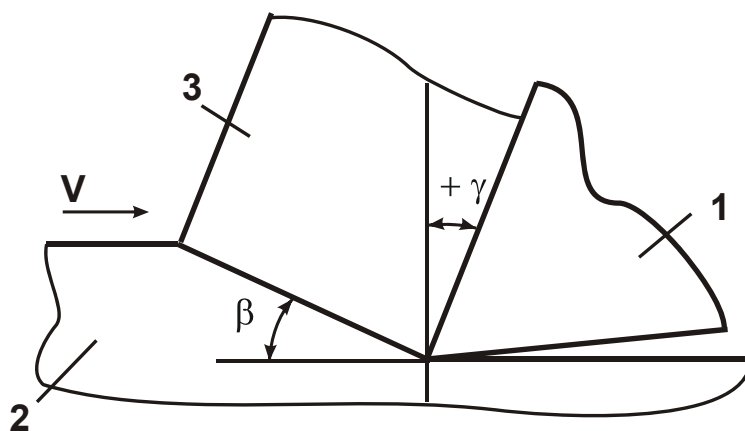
Расчетная схема параметров процесса резания: 1 – резец; 2 – обрабатываемый материал; 3 – образующаяся стружка
